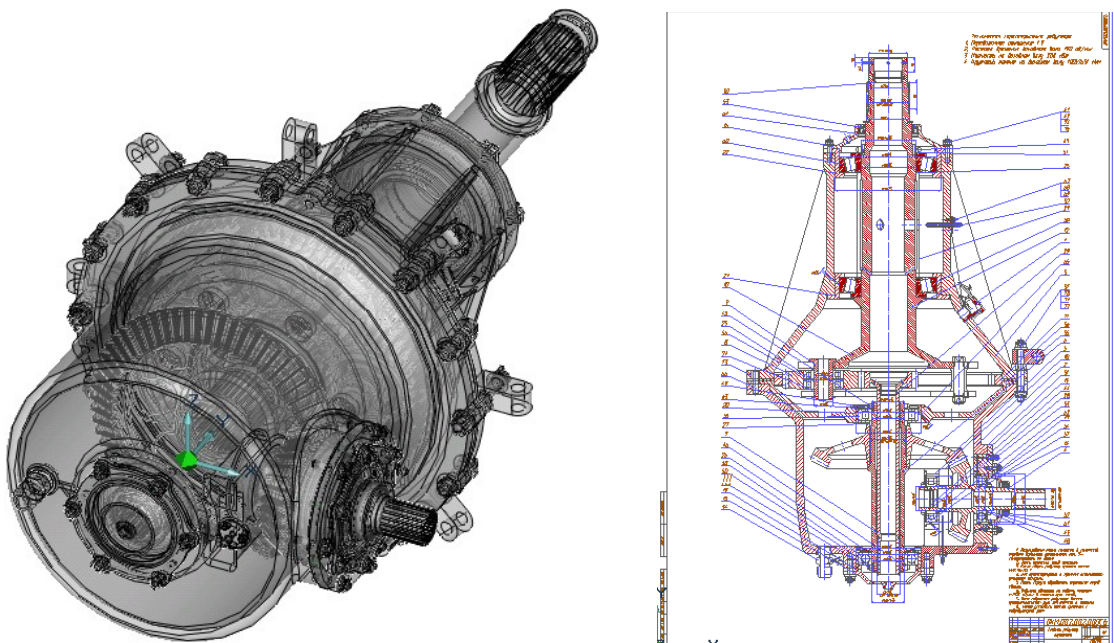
3D модель редуктора в сборе и созданный на ее основе сборочный чертеж
